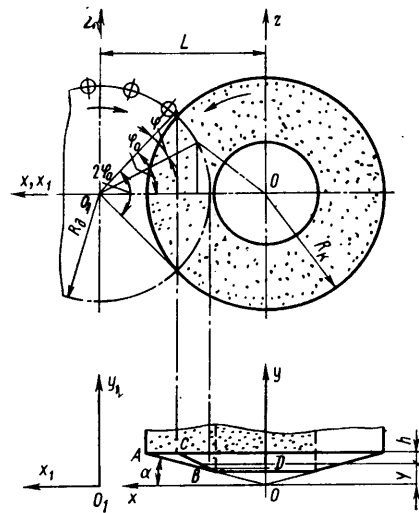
Схема для определения закономерностей съема припуска при шлифовании кругами с конической рабочей поверхностью
